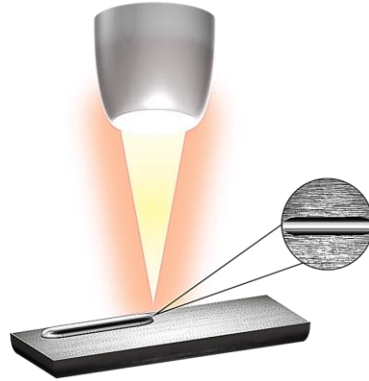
Esquema de micro-soldadura continua.
